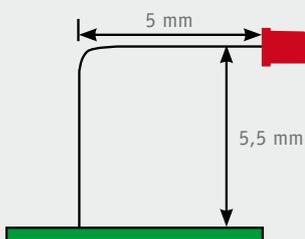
Die Anschlüsse der LEDs sind wie hier gezeigt abzuwinkeln.
